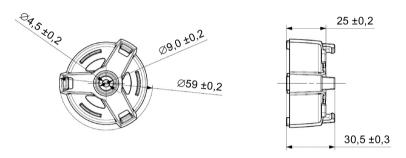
Desenho de dimensões do espaçador 6GT2690-0AL00
